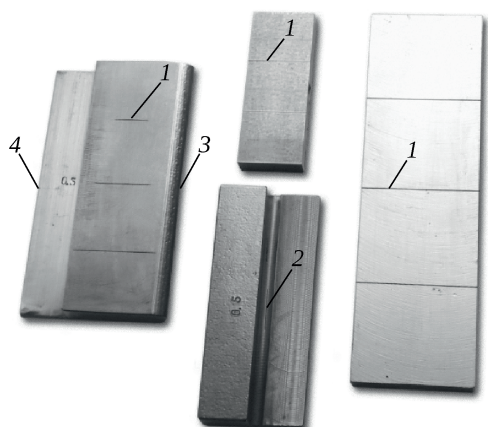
Образцы, используемые для настройки и проверки вихретоковых дефектоскопов, с модельными дефектами (надрезами): 1 – на плоской поверхности; 2 – на поверхности паза; 3 – на выпуклой поверхности; 4 – на кромке
